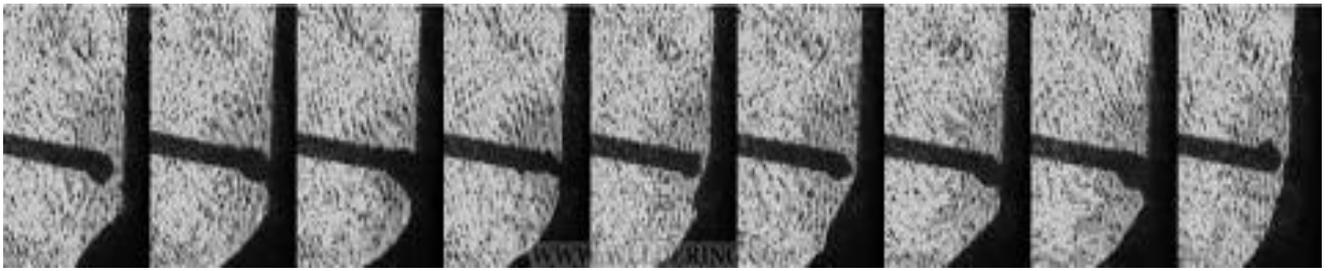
Сварка в вертикальном положении[48]
